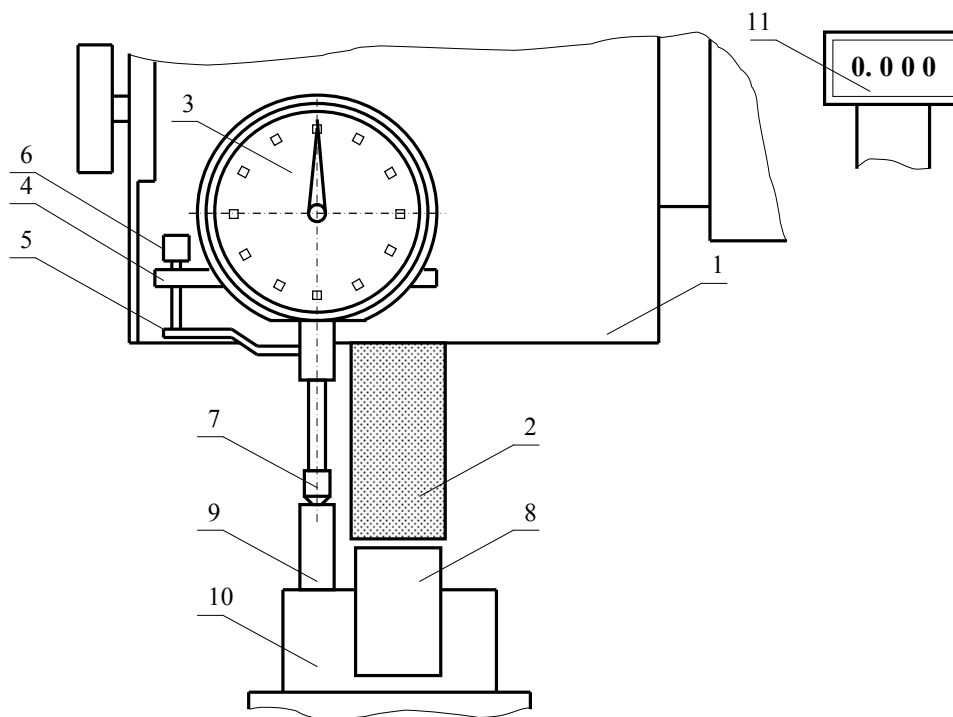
Проверка исходного положения обрабатываемого образца с помощью механического индикатора
